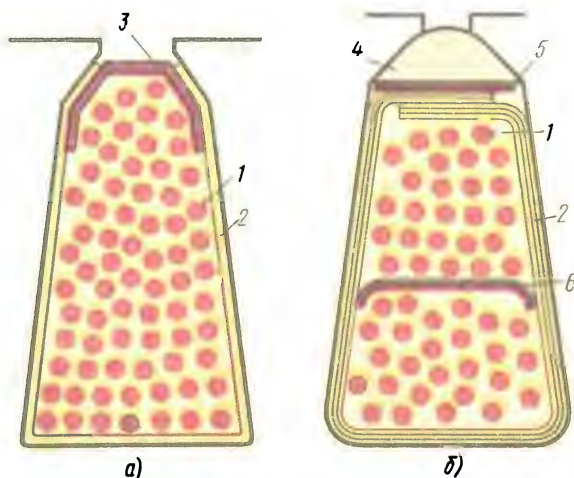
Поперечные сечения полузакрытых пазов с обмоткой из круглого провода:
